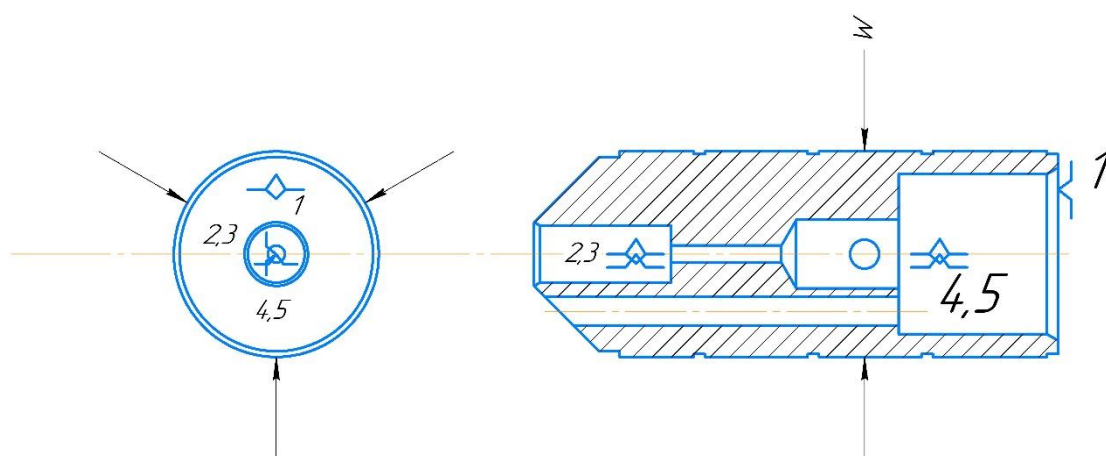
Принципиальная схема зажима заготовки в приспособлении
